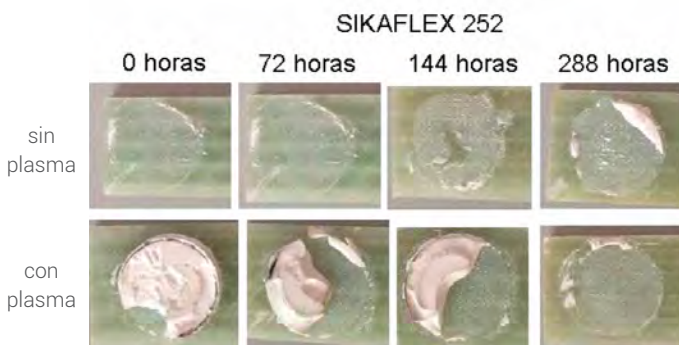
Roturas de las probetas por pull-off con adhesivo de PU
